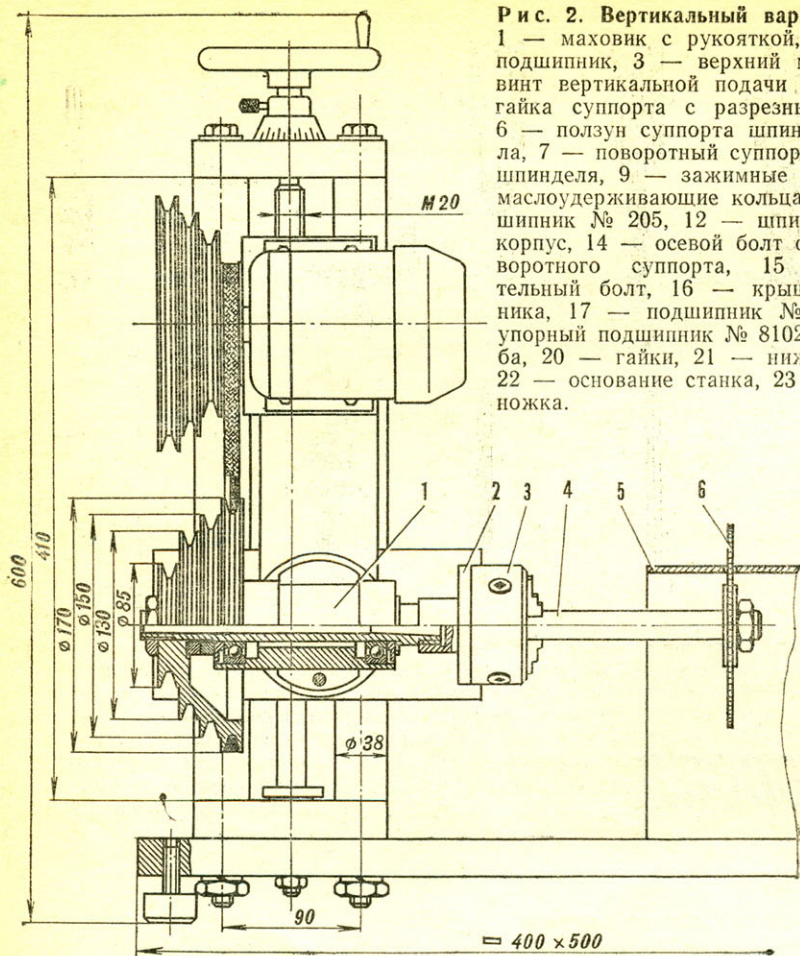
Вертикальный вариант станка: 1 — маховик с рукояткой, 2 — лимб-подшипник, 3 — верхний мостик, 4 — винт вертикальной подачи (M20), 5 — гайка суппорта с разрезным фланцем, 6 — ползун суппорта шпиндельного узла, 7 — поворотный суппорт, 8 — шкив шпинделя, 9 — зажимные гайки, 10 — маслоудерживающие кольца, 11 — подшипник № 205, 12 — шпиндель, 13 — корпус, 14 — осевой болт фиксации поворотного суппорта, 15 — дополнительный болт, 16 — крышка подшипника, 17 — подшипник № 202, 18 — упорный подшипник № 8102, 19 — шайба, 20 — гайки, 21 — нижний мостик, 22 — основание станка, 23 — винтовая ножка.
